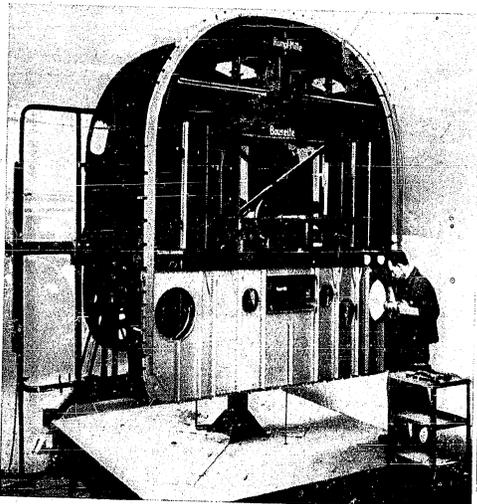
Schwenkbare Spantbauvorrichtung auf Rohrbasis. Die Querträger sind auf genormten Kastenschellen befestigt
